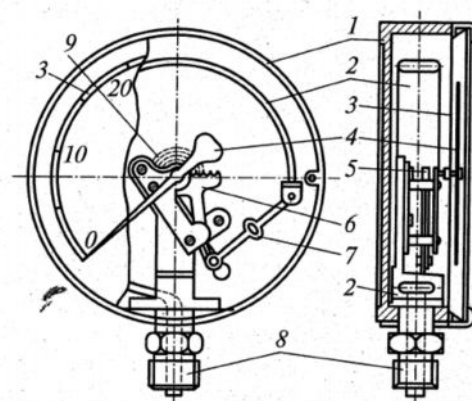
Устройство пружинного манометра: 1-корпус; 2-полая труба; 3-шкала; 4-стрелка; 5-шестерня; 6-зубчатый сектор; 7-поводок; 8-штуцер; 9- пружина
